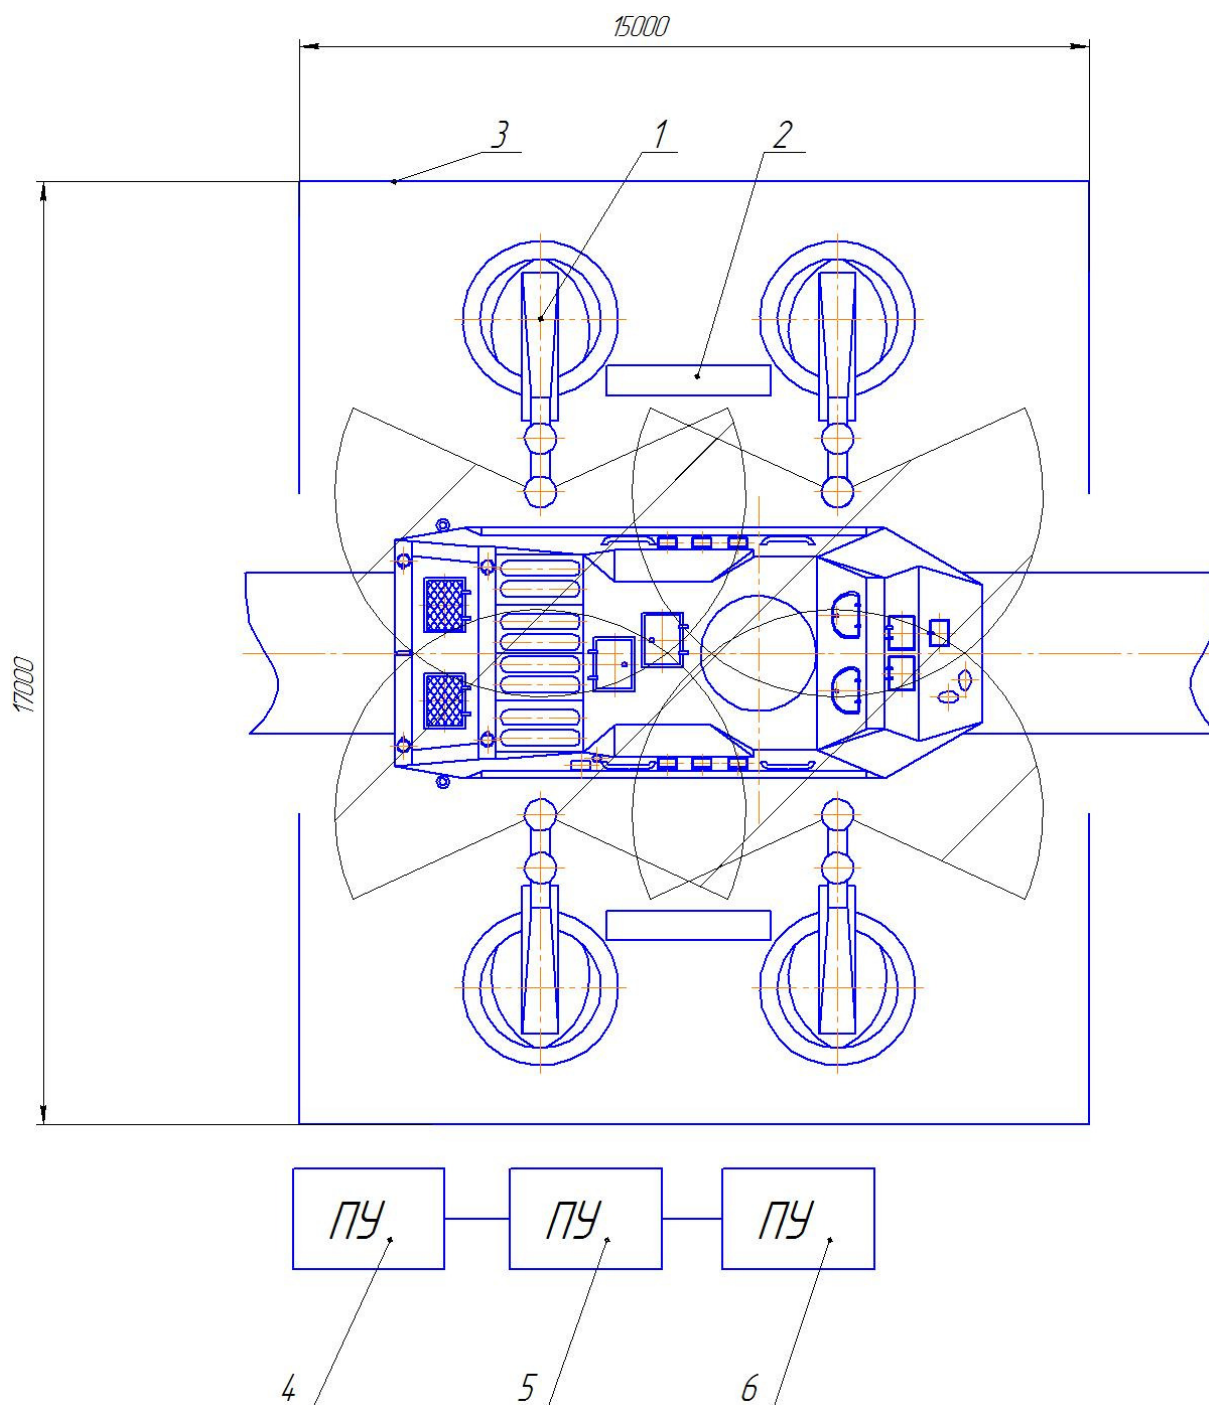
Компоновка камеры покраски корпуса БТР
